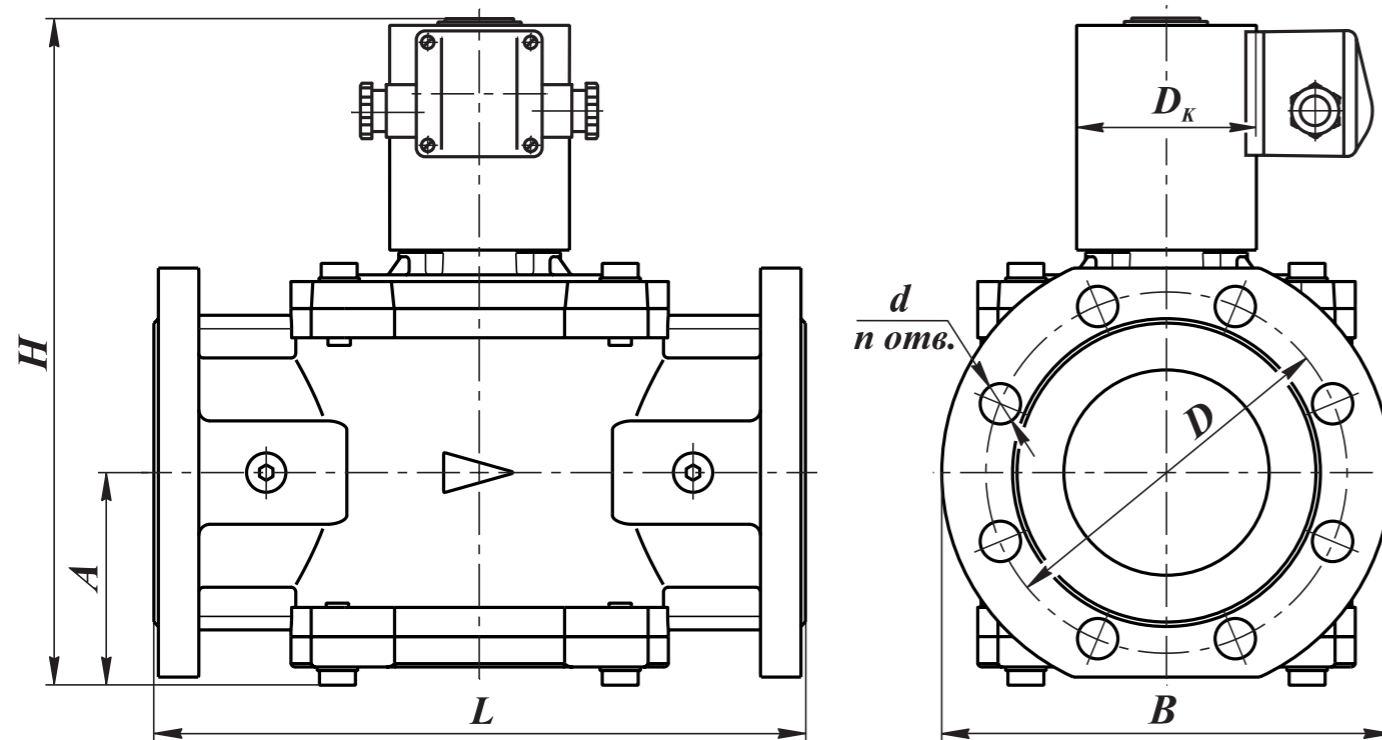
Клапаны на DN 50 - 100 фланцевые (исполнение: с присоединительными фланцами PN16)
